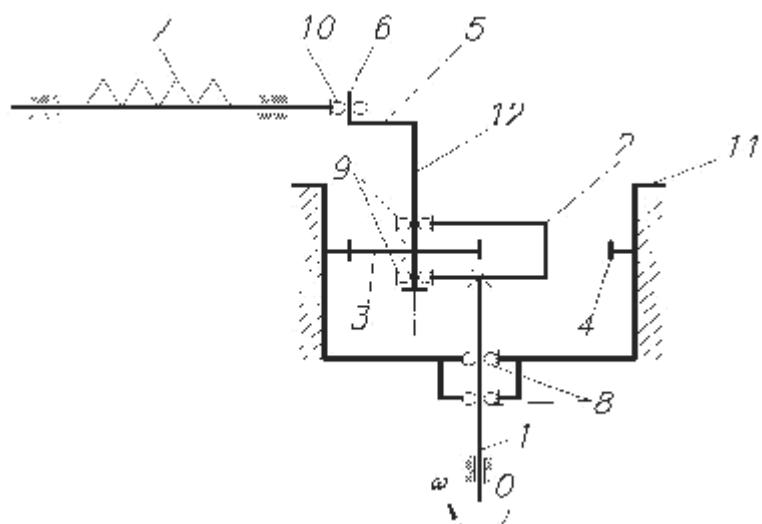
Кинематическая схема планетарного механизма привода ножа.
